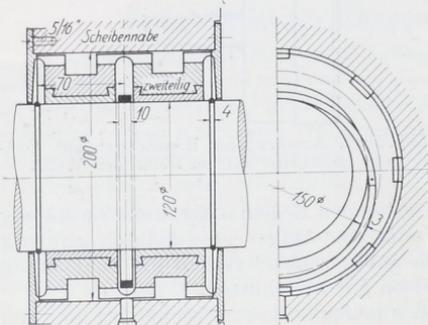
Leerlaufbüchse mit Ringschmierung. Prager Maschinenbau-A. G. M. 1:5.
